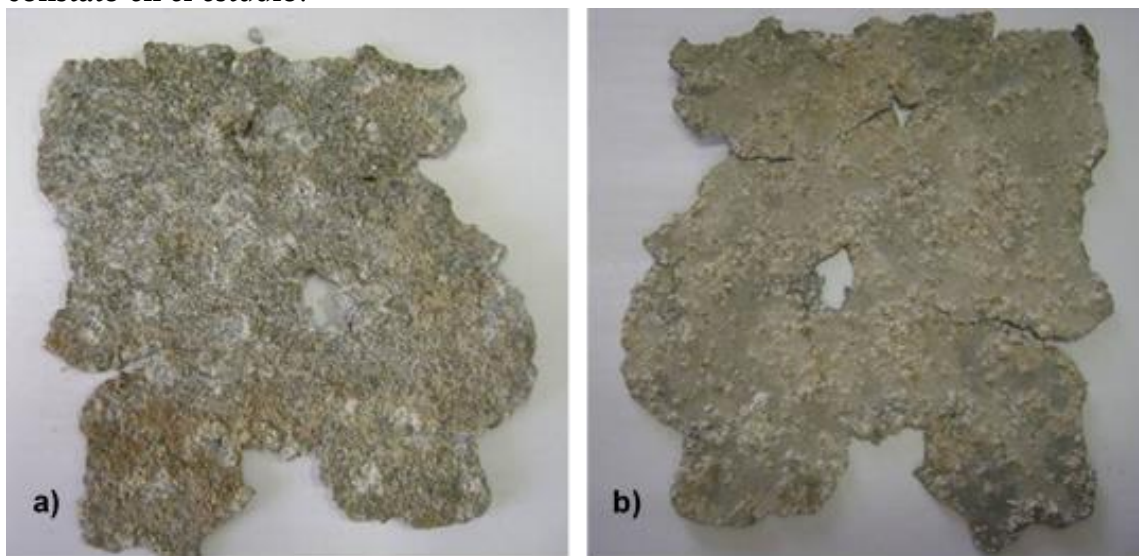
Muestra de la zona de falla de una de las planchas de aluminio, a) parte superior de la plancha y b) parte inferior de la plancha.
